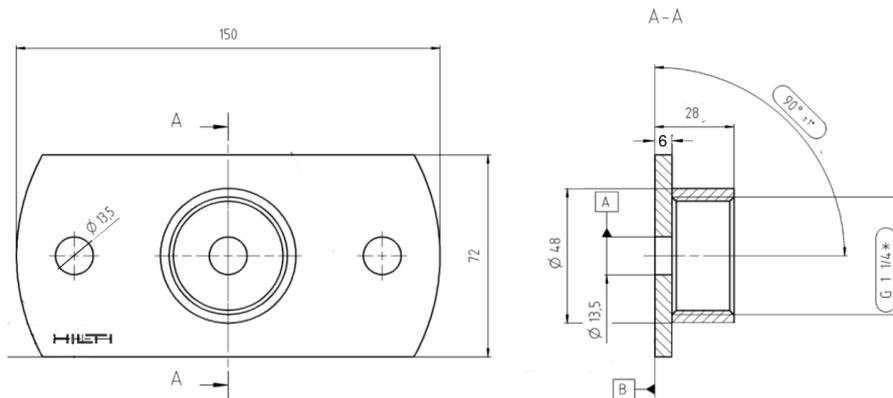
Hilti Fixpunktsystem „universal“ MFP-U: Festpunktgrundplatte inklusive angeschweißter Gewindemuffe 1 1/4"
